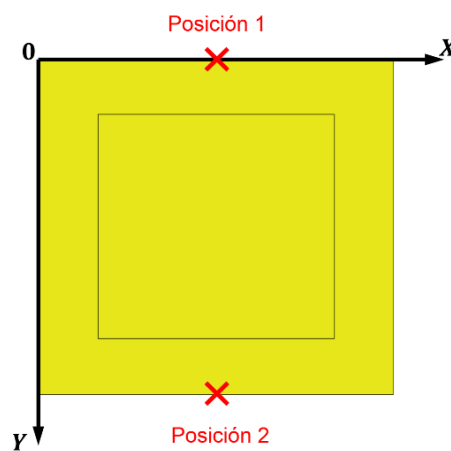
Vista de planta de la viga impresa donde se muestran en rojo las posiciones del extrusor que se utilizaron para determinar las características mecánicas de los resortes de las prensas/carros.
